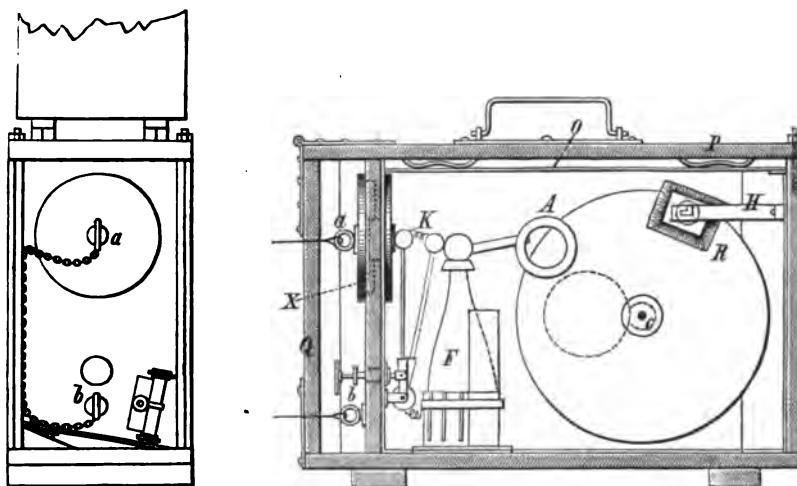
und 252. Bornhardt'sche Zündmaschine.
